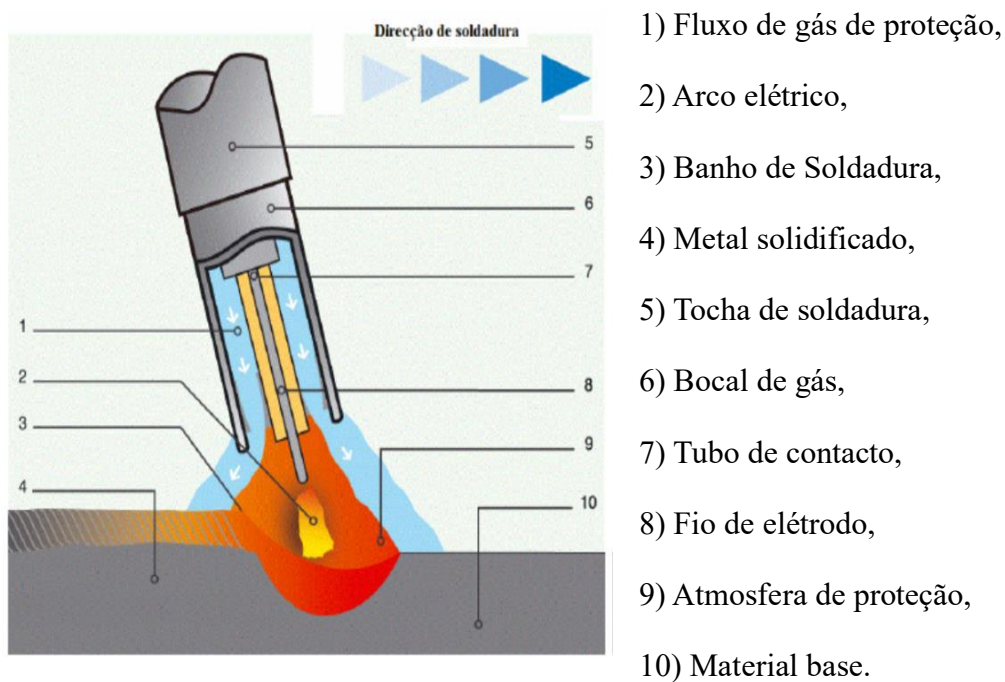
Processo soldadura MIG/MAG [9]
